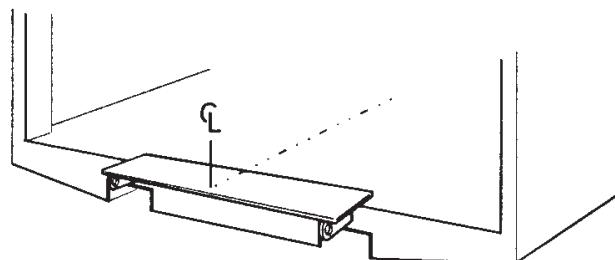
Skruva eller punktsvetsa monteringsjiggen vid bakbalken
